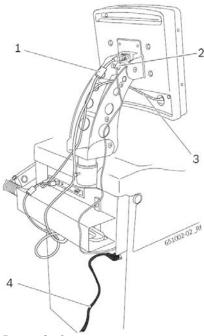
Соединение монитора и клавиатуры со станком для балансировки колес WBE 4415:
